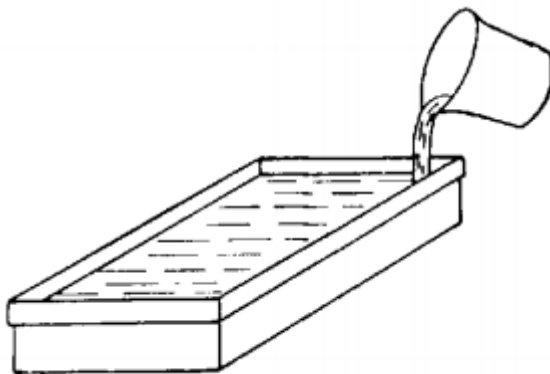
Схема заливки рідкого металу на тверду пластину.
